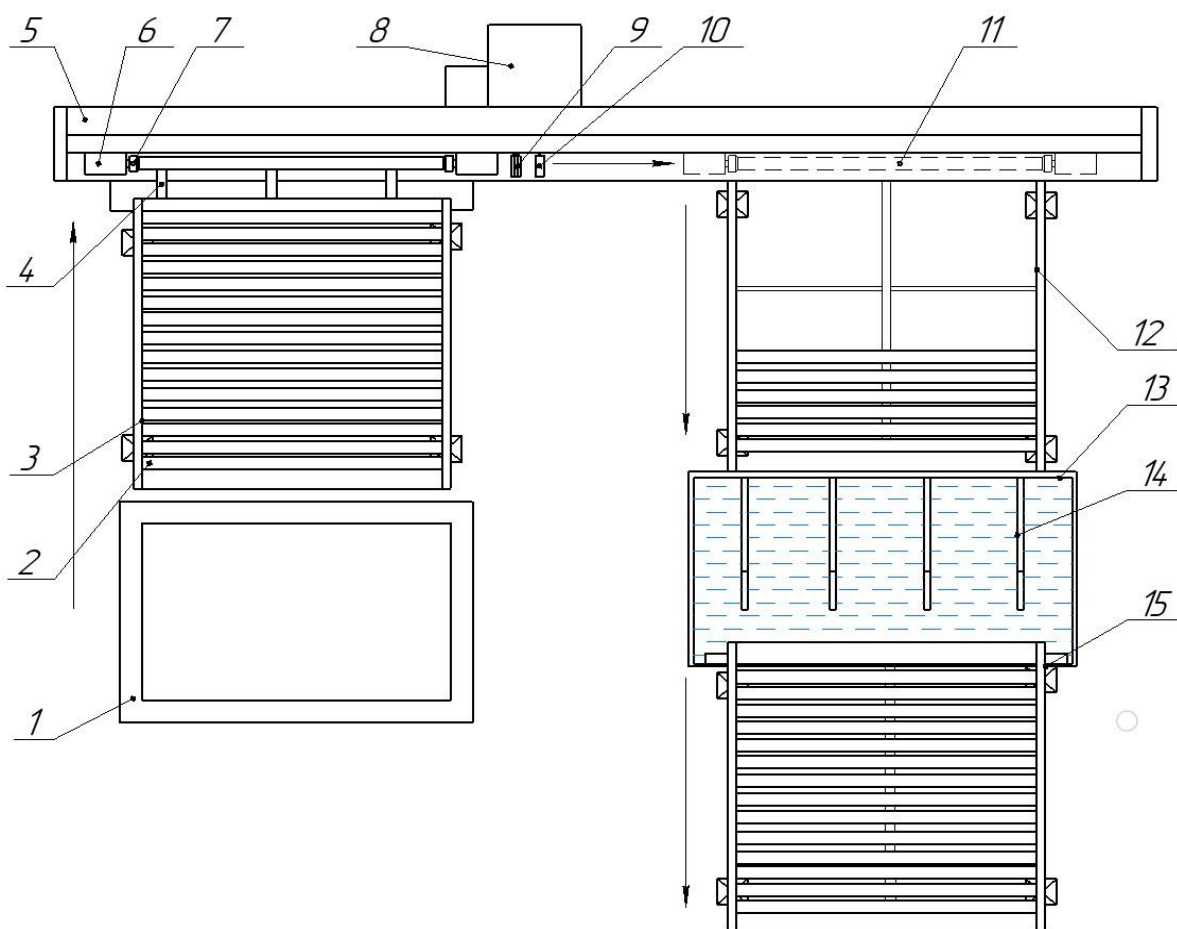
Схема установки ТВЧ для термической обработки трубных заготовок
